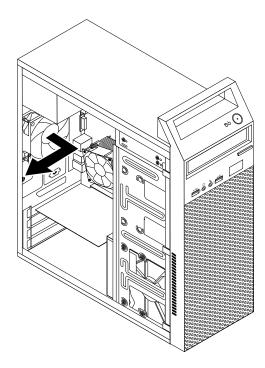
Rimozione dell'assieme di ventilazione posteriore
